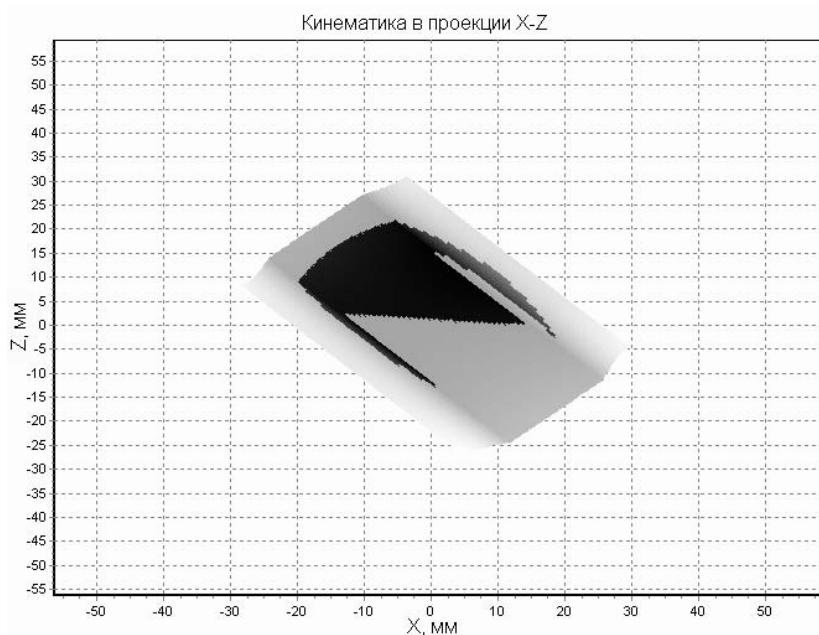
Визуализация процесса нарезания винтовой поверхности дисковой фрезой
